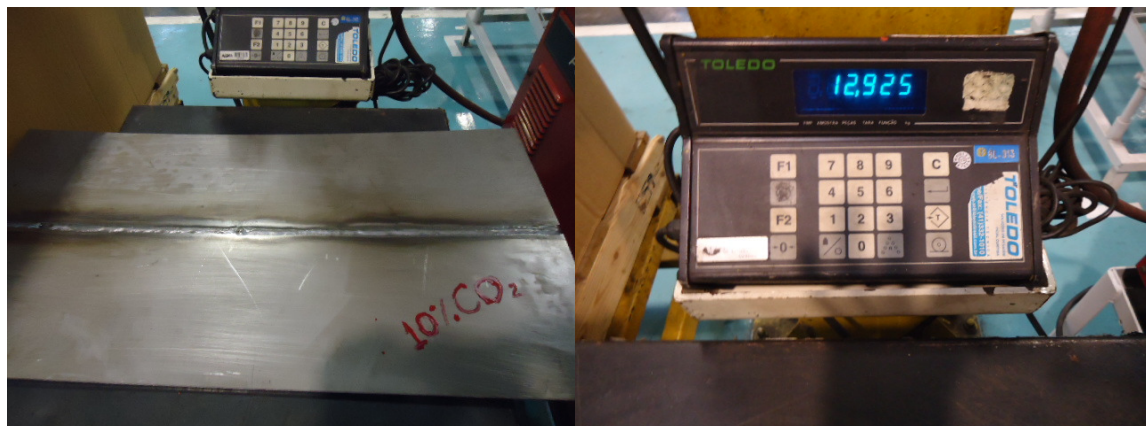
Chapa após a soldagem com mistura 10% CO₂
